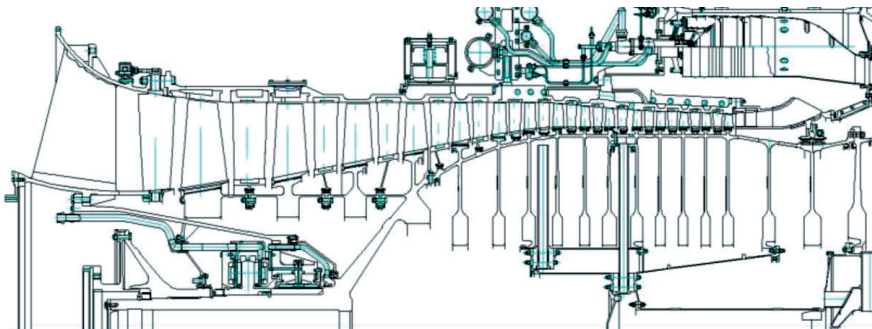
Продольный разрез компрессора двигателя ГТД-110
